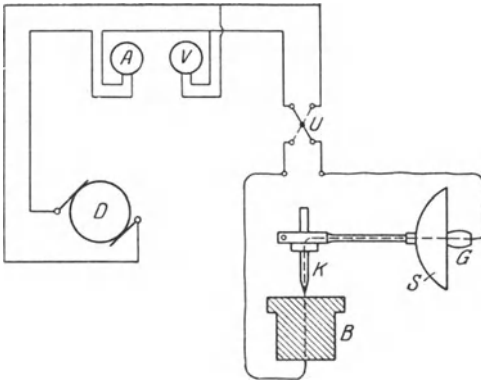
Schema einer Lichtbogenschweißanlage.
